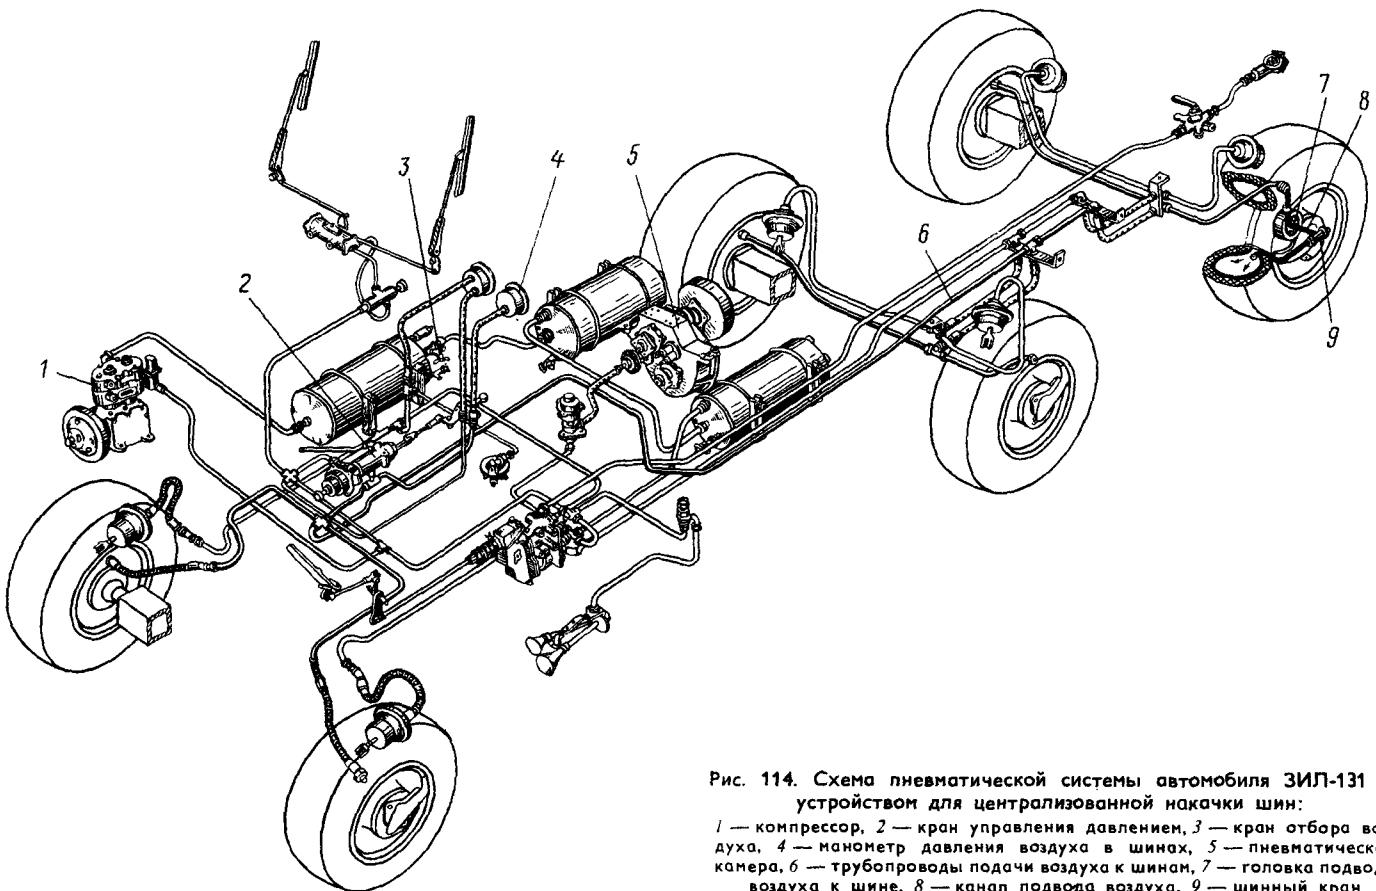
Схема пневматической системы автомобиля ЗИЛ-131 с устройством для централизованной накачки шин:
